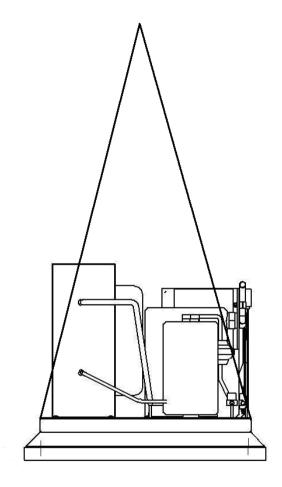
Агрегат компрессорно-конденсаторный ИПКС-116. Схема строповки.
